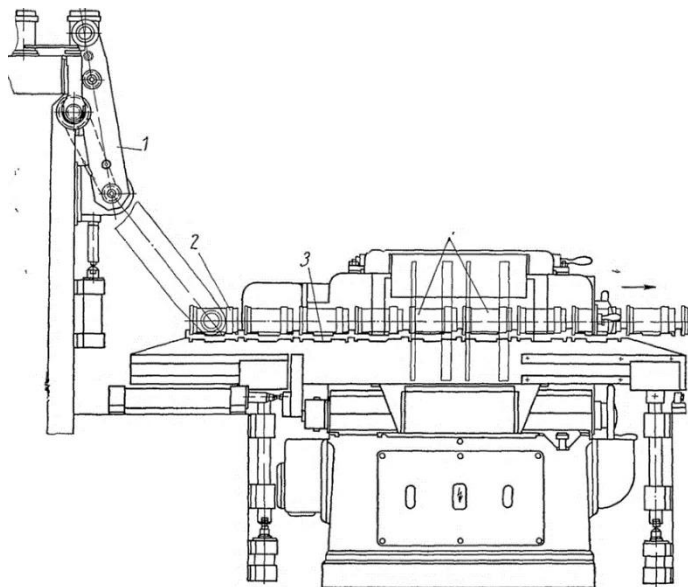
Автоперегрузчик гильз и автооператор бесцентрово-шлифовального станка:
